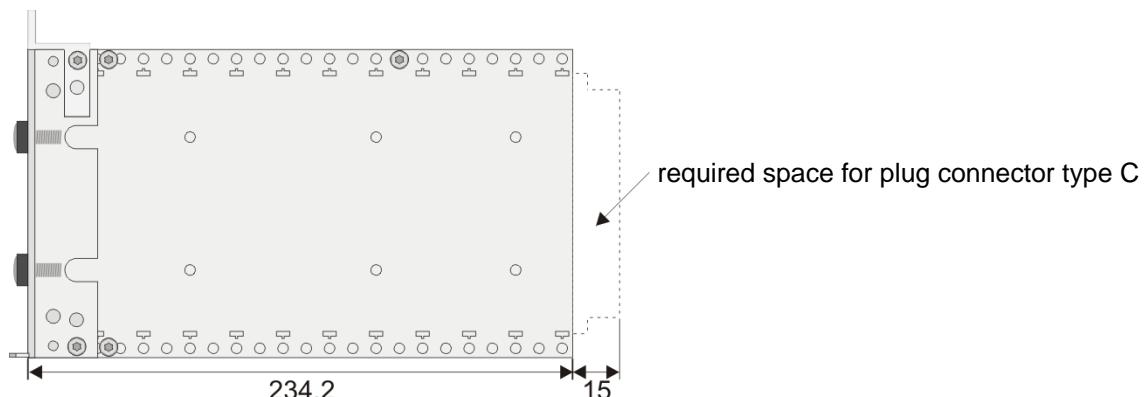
Side view of the board rack BGT08 with label bar, measurements in mm
